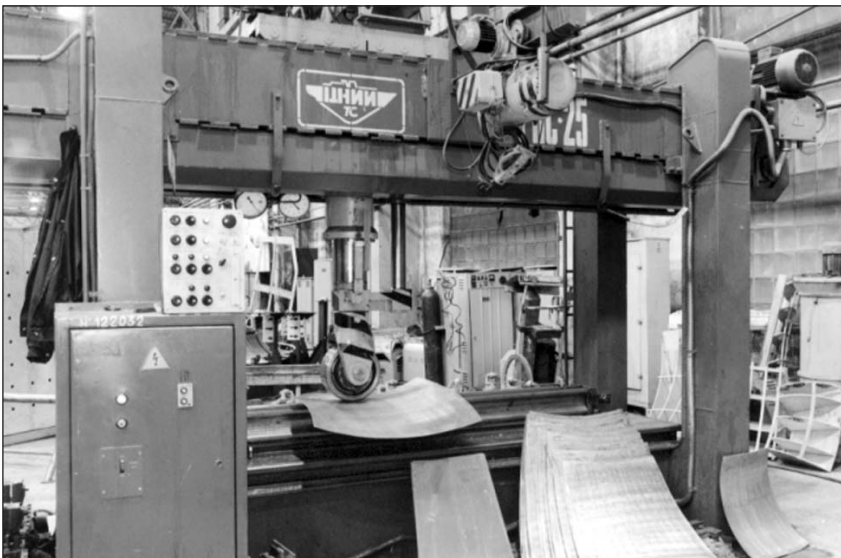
Гибка на станке МГПС-25 листовых деталей для обшивки диффузора
